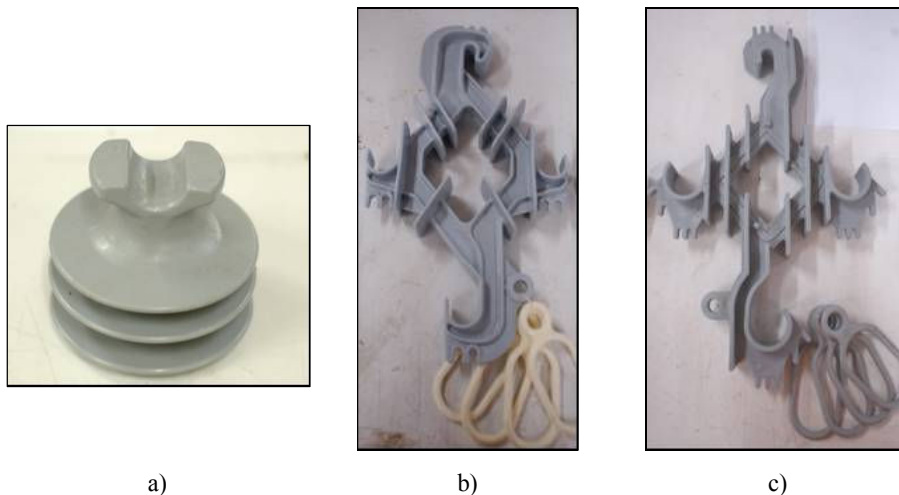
a) isolador polimérico do fabricante b, b) conjunto espaçador-amarração do fabricante c e c) conjunto espaçador-amarração do fabricante b
